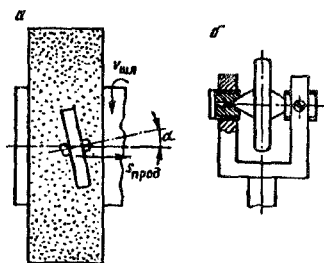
Схема правки круга обкатыванием (а) и инструмент (б)
